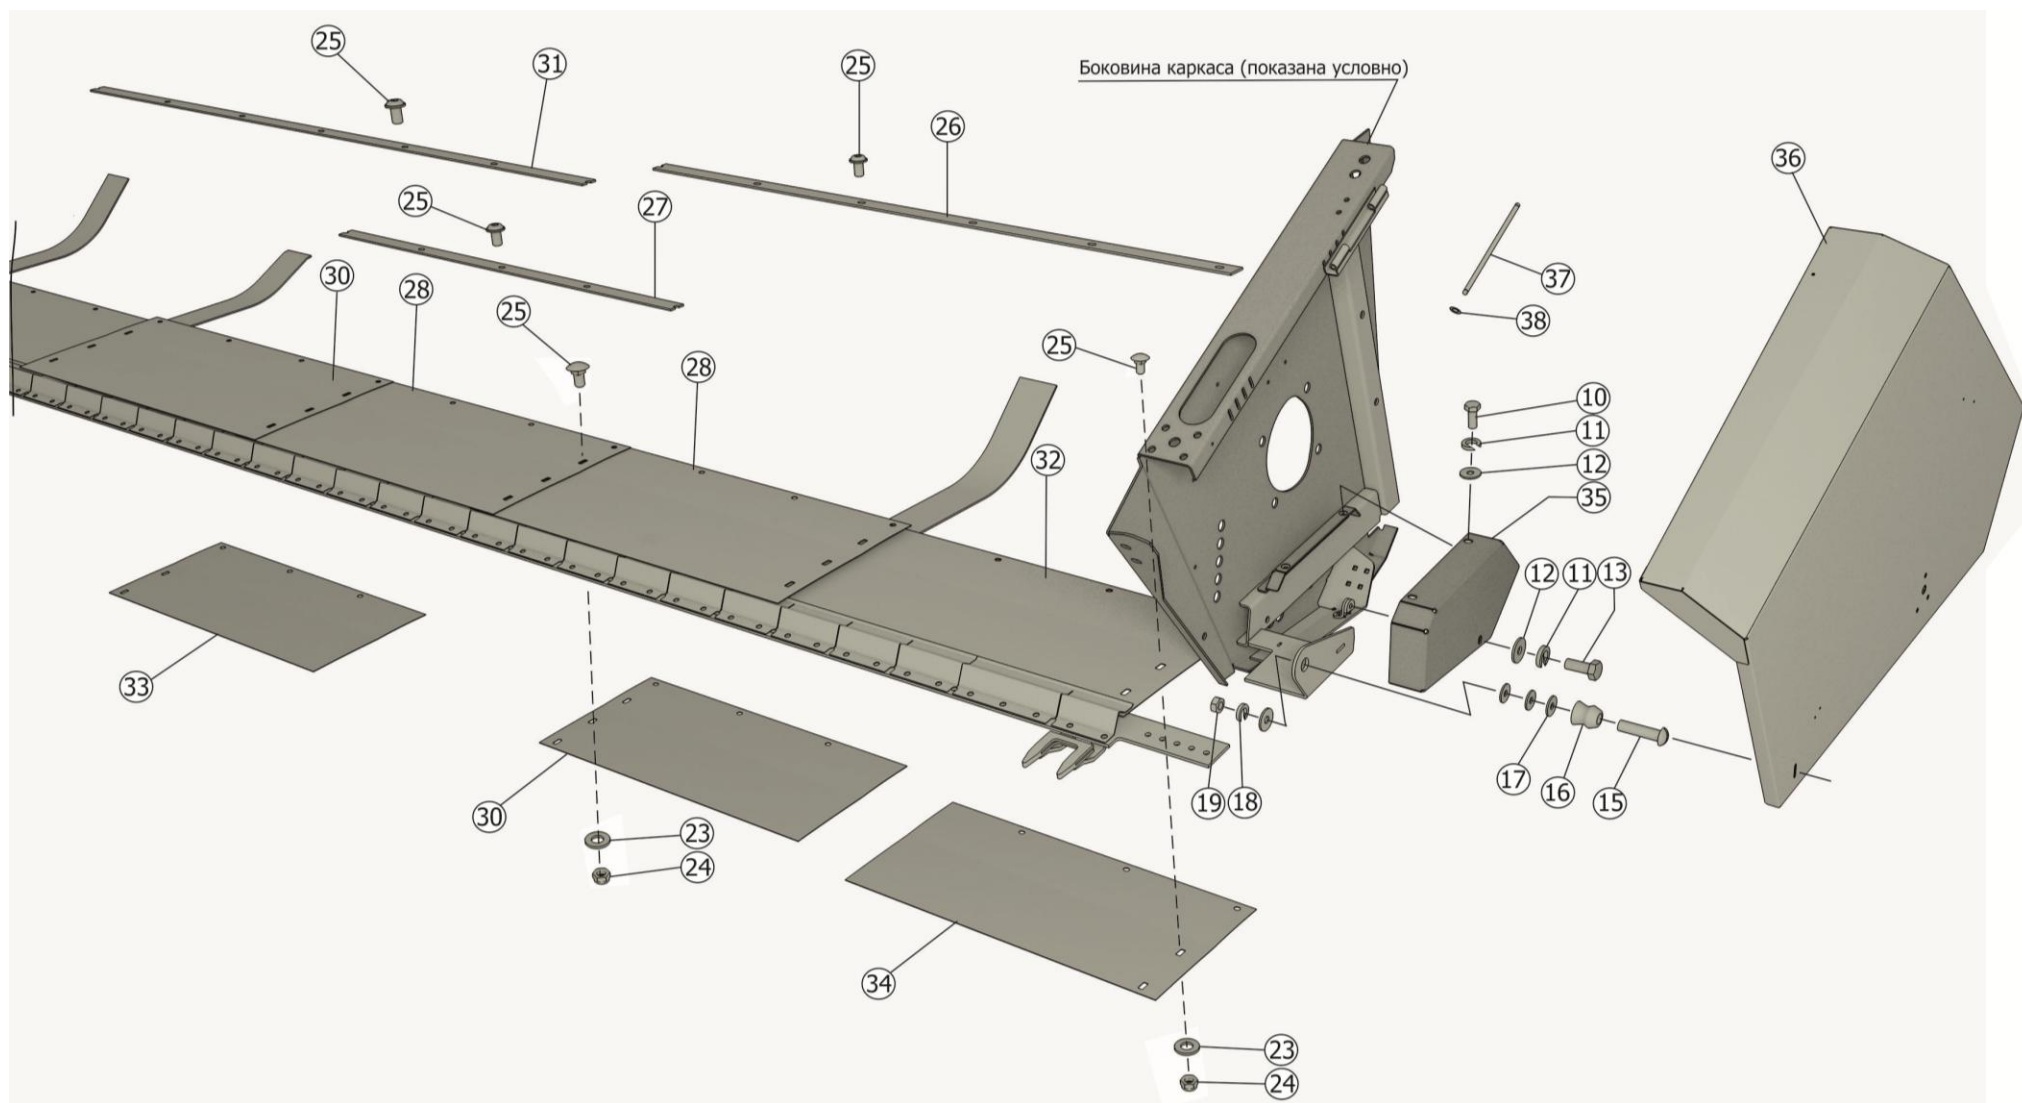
Установка щитков ЖСУ-703.11.00.000Б. Левая сторона
